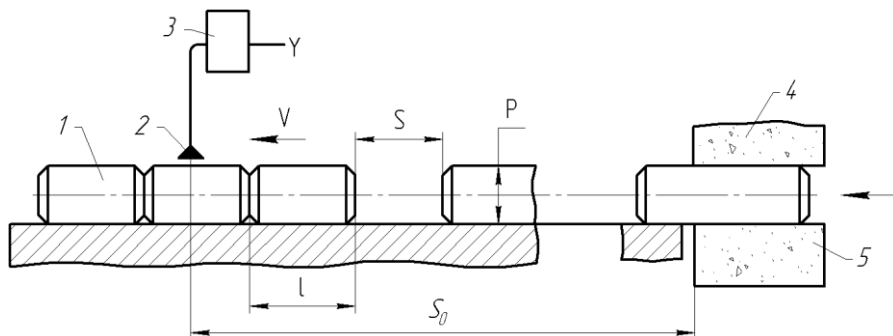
Схема активного контроля, управляющего автоматической подналадкой бесцентровошлифовального станка /2/
